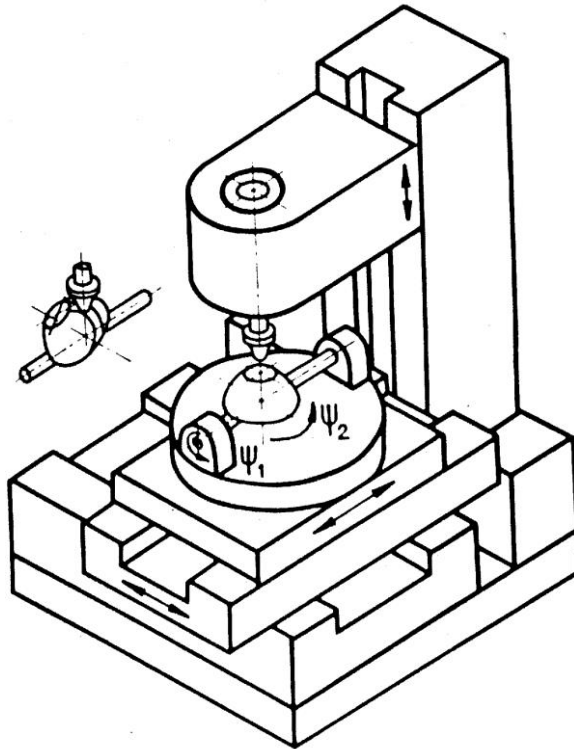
Компоновка станка для первой кинематической схемы формообразования
